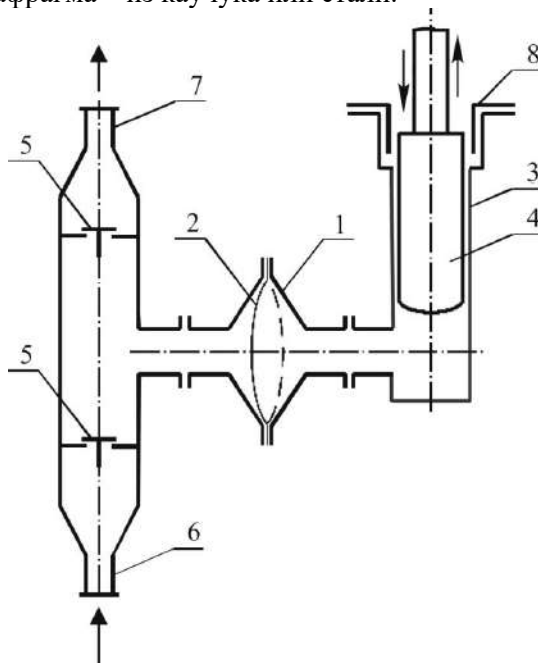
Диафрагмовый насос: 1 – корпус; 2 – диафрагма (мембрана); 3 – цилиндр; 4 – плунжер; 5 – клапаны; 6, 7 – всасывающий и нагнетательный патрубки; 8 – сальниковые уплотнители.
